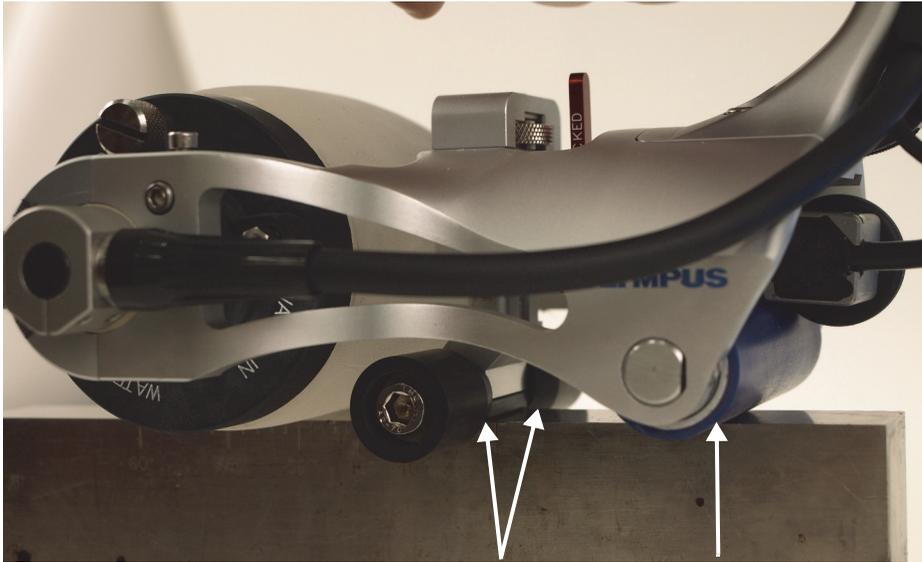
Manter os dois roletes em contato com uma superfície convexa
